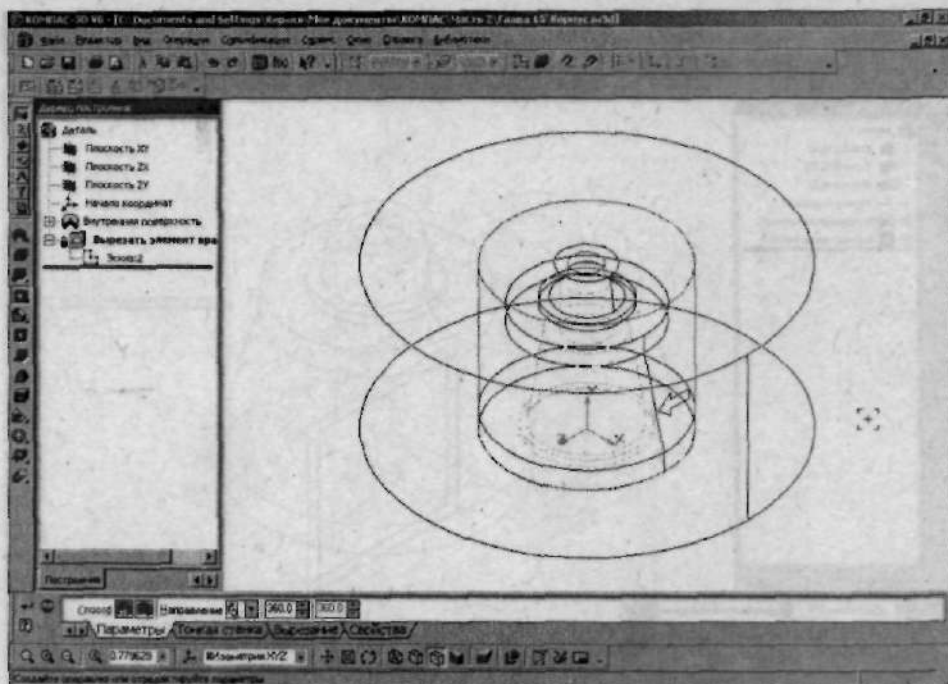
Сформируйте внешнюю поверхность Корпуса
